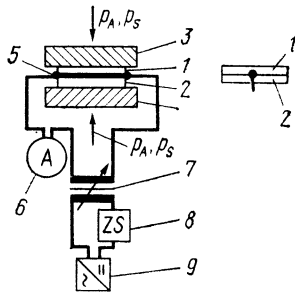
Сварка панелей нагретой проволокой: 1, 2 — свариваемые детали; 3, 4 — нажимные плиты; 5 — нагретая проволока (нихром или медь); 6 — измеритель тока; 7 — регулировочный трансформатор; 8 — реле времени; 9 — источник питания
